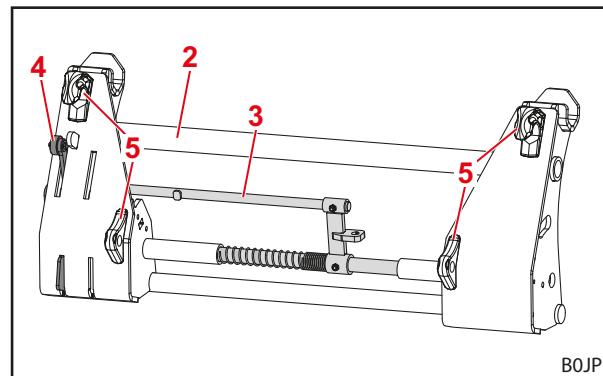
Aufbau MX-Werkzeugadapter – Rückansicht
